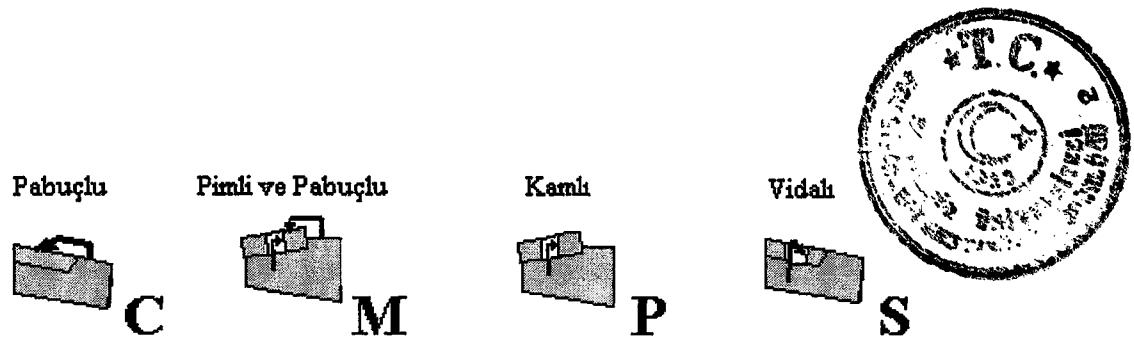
İç ve dış tornalama için takım tutucu ve kesici uçların ISO kodları
